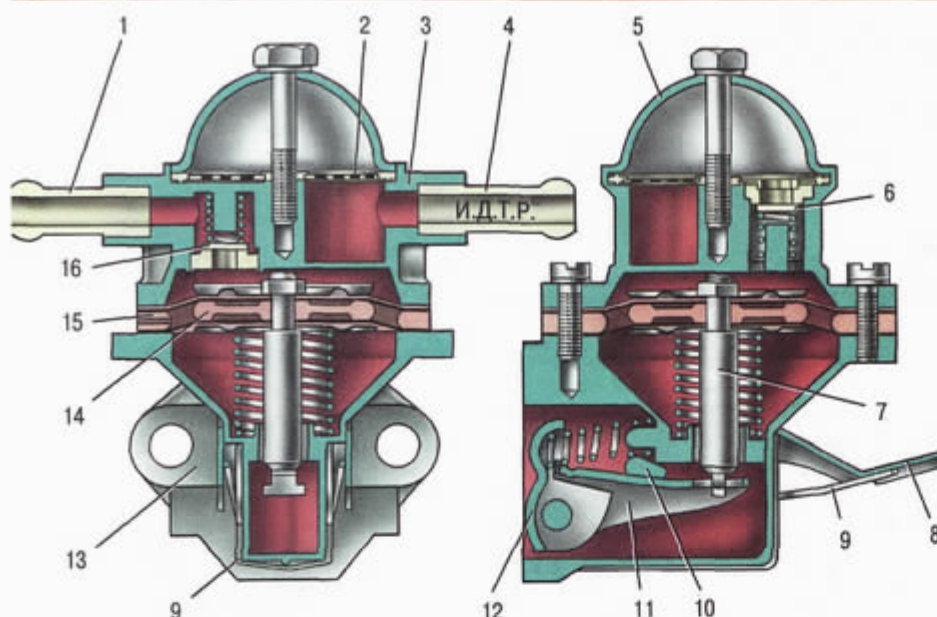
Топливный насос: 1 – нагнетательный патрубок; 2 – фильтр; 3 – корпус; 4 – всасывающий патрубок; 5 – крышка; 6 – всасывающий клапан; 7 – шток; 8 – рычаг ручной подкачки топлива; 9 – пружина; 10 – кулачок; 11 – балансир; 12 – рычаг механической подкачки топлива; 13 – нижняя крышка; 14 – внутренняя дистанционная прокладка; 15 – наружная дистанционная прокладка; 16 – нагнетательный клапан
